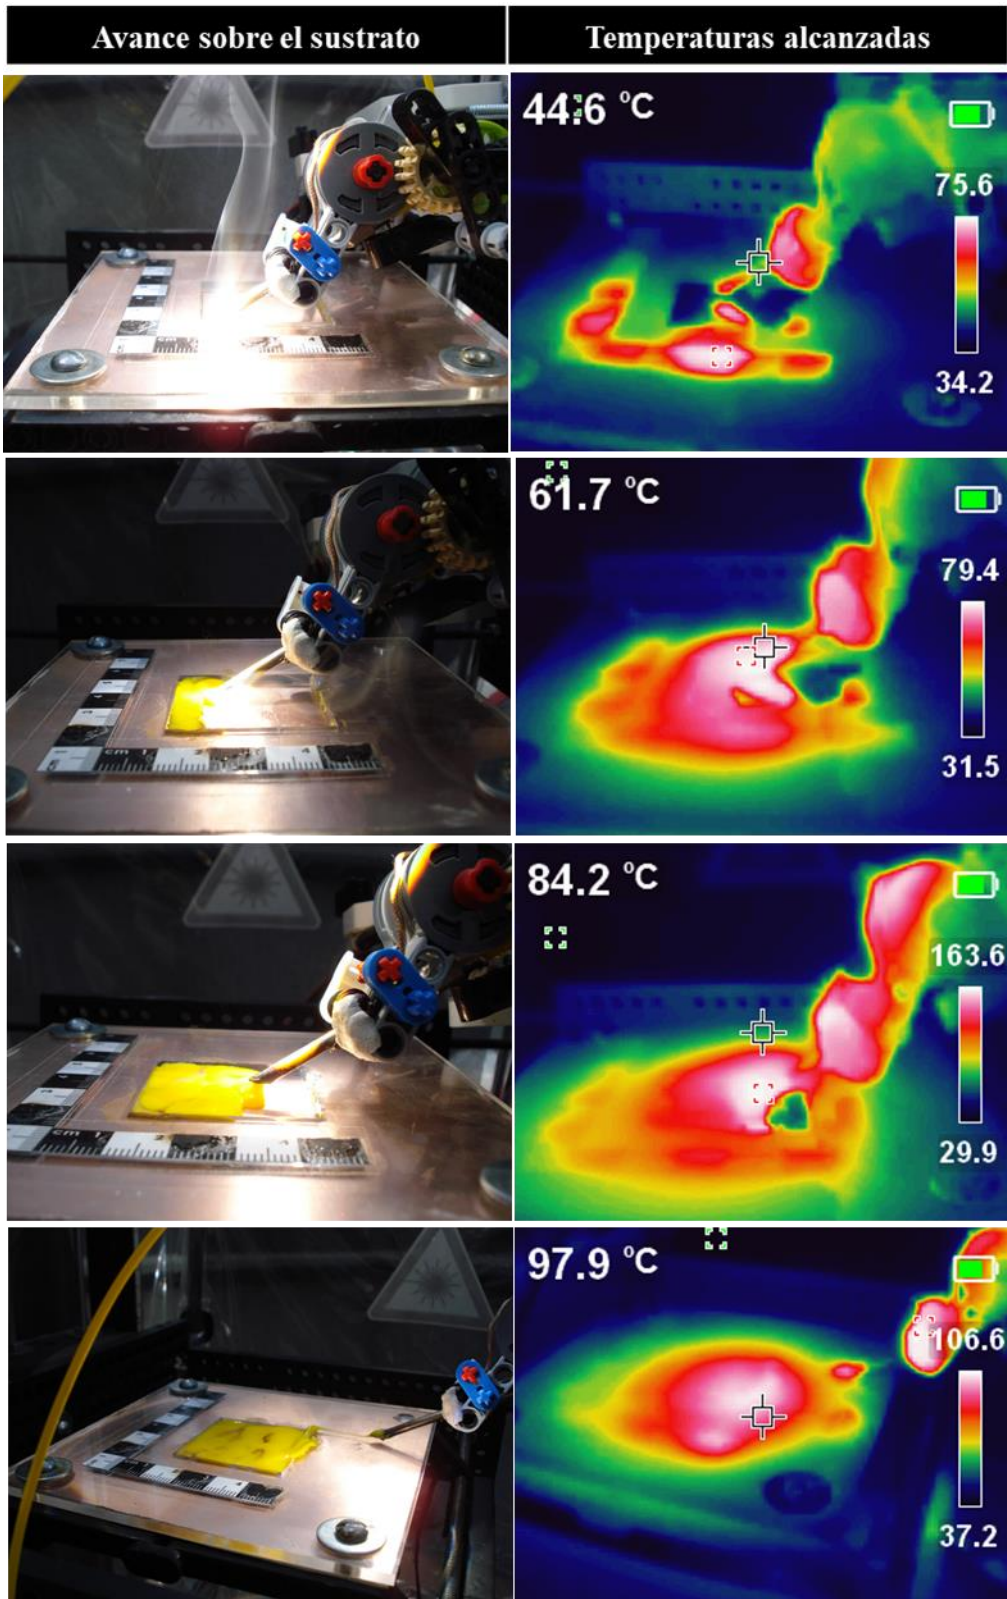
Secuencia para la deposición de PCL sobre el molde cuadrado.
